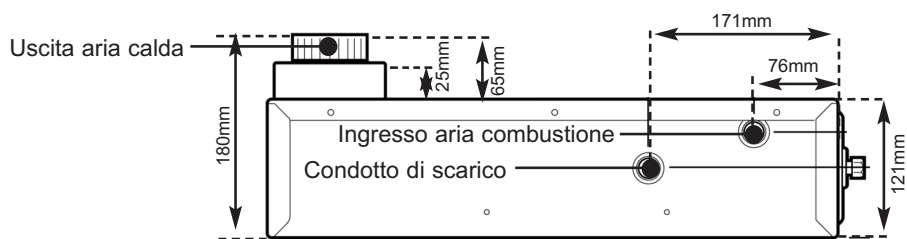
Installazione sotto il pavimento – Vista laterale - SH2211 o SC2211
